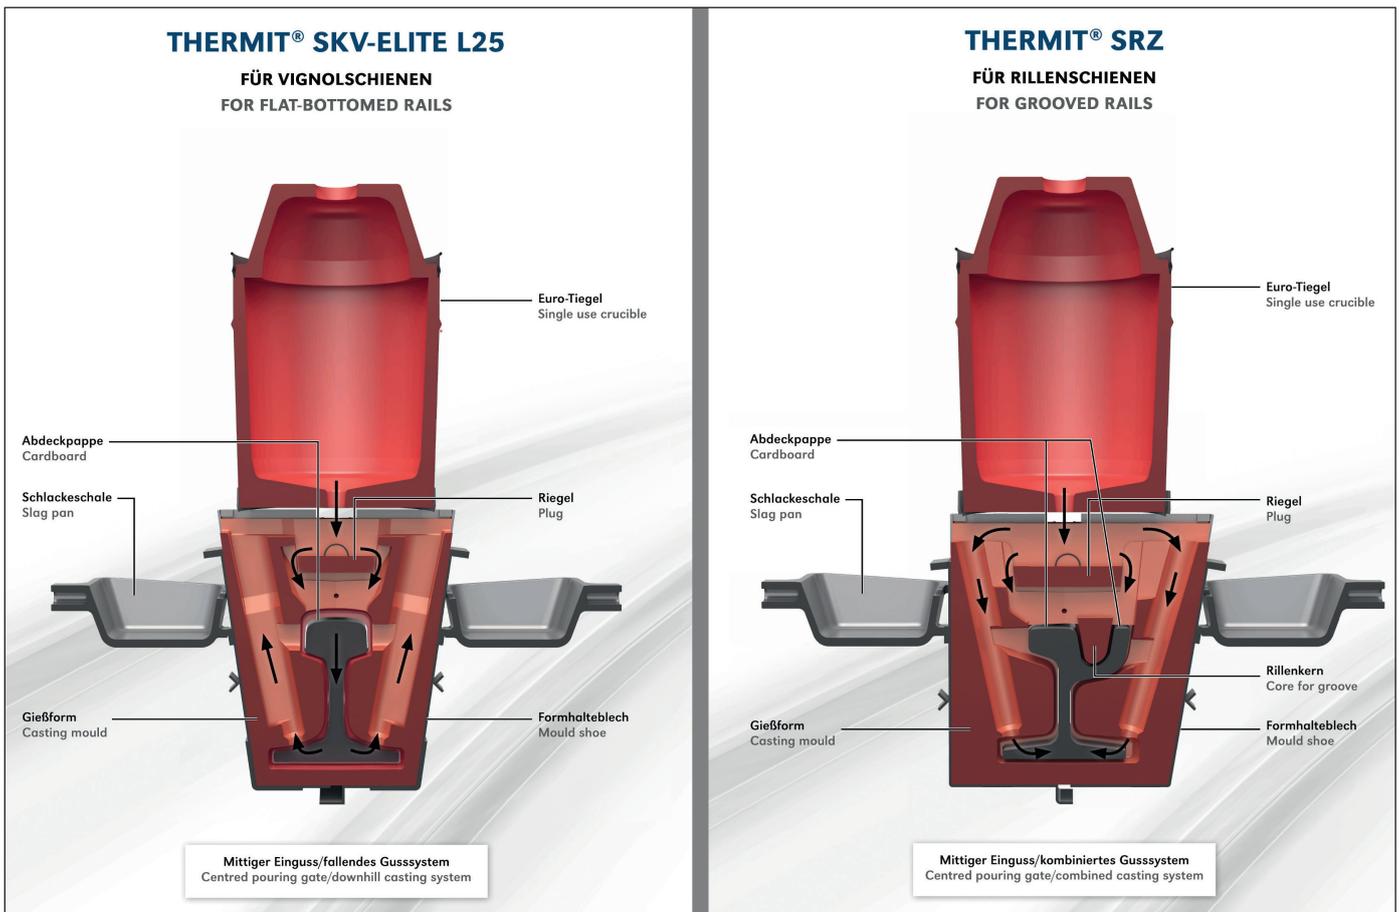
Gießschemata von Thermo-Schweißverfahren
